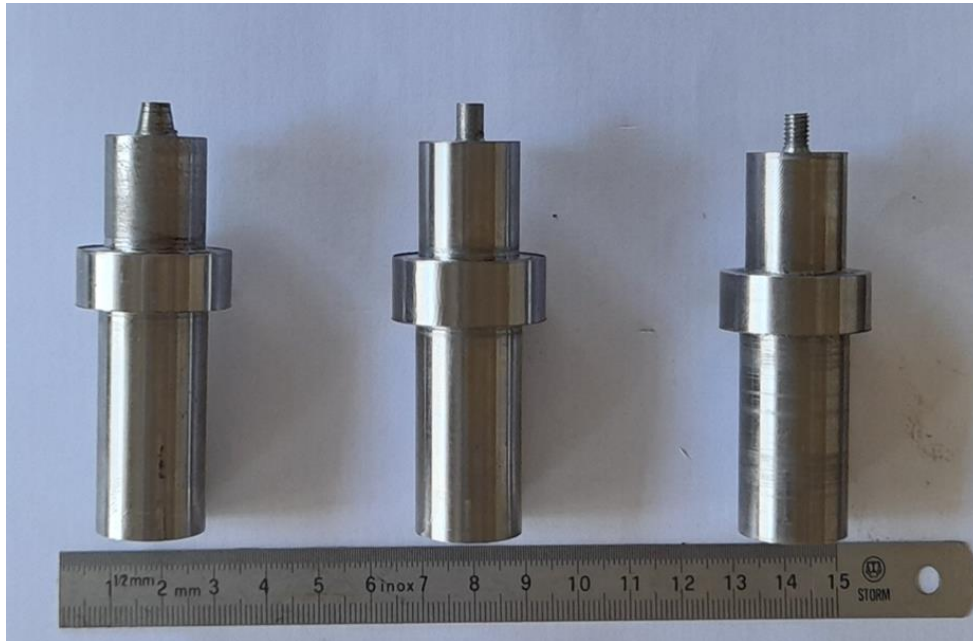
Les outils de soudage de FSW utilisés.
